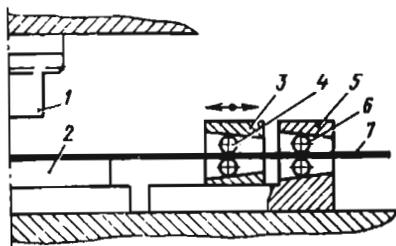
Схема ролико-клиновой подачи: 1 — прунсон; 2 — матрица; 3 — подающая каретка; 4 — ролики; 5 — корпус тормоза обратного хода; 6 — ролики тормоза; 7 — лента
